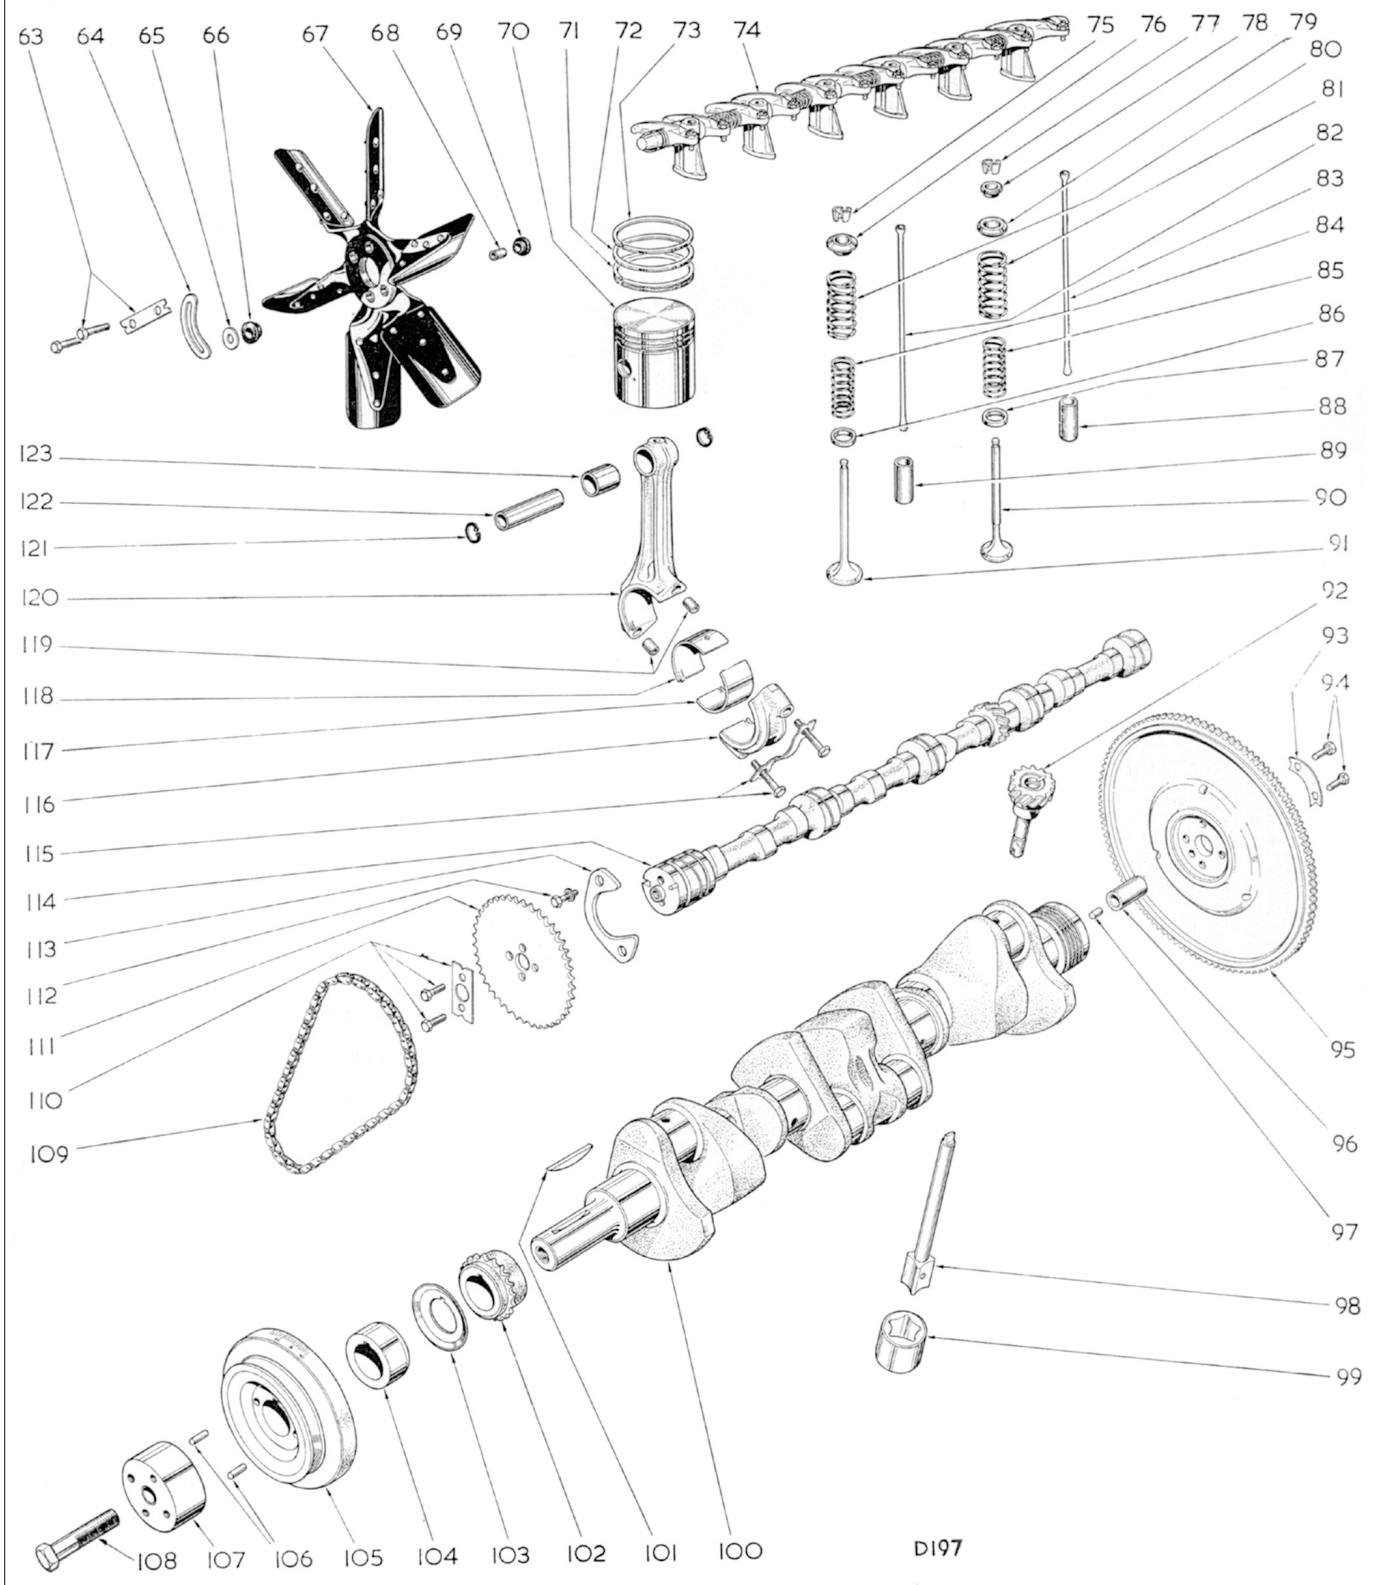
Pièces mobiles du moteur (Vitesse)
